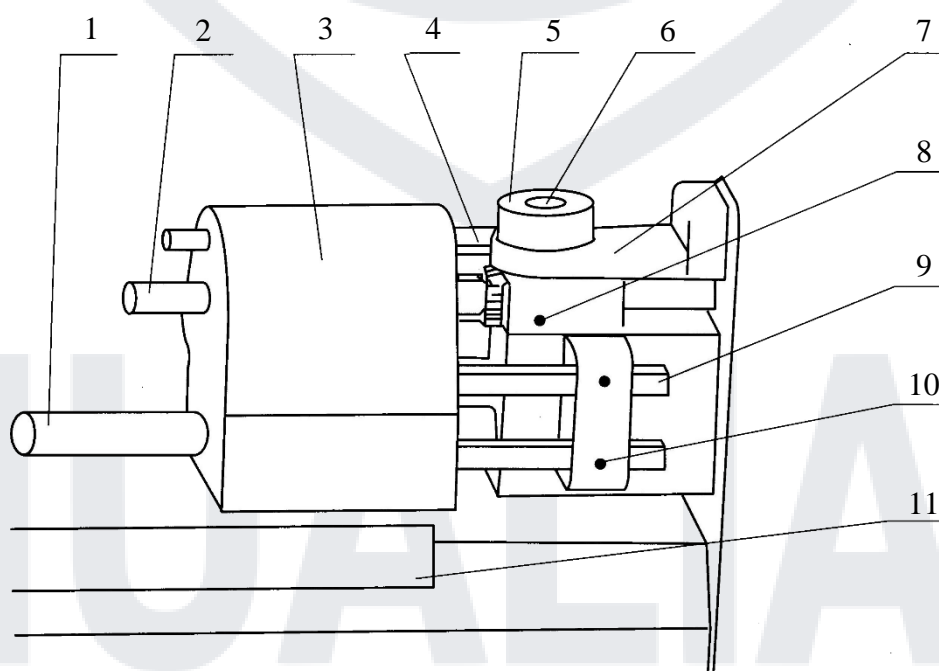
Регулировка расстояния печатающего колеса и ролика
